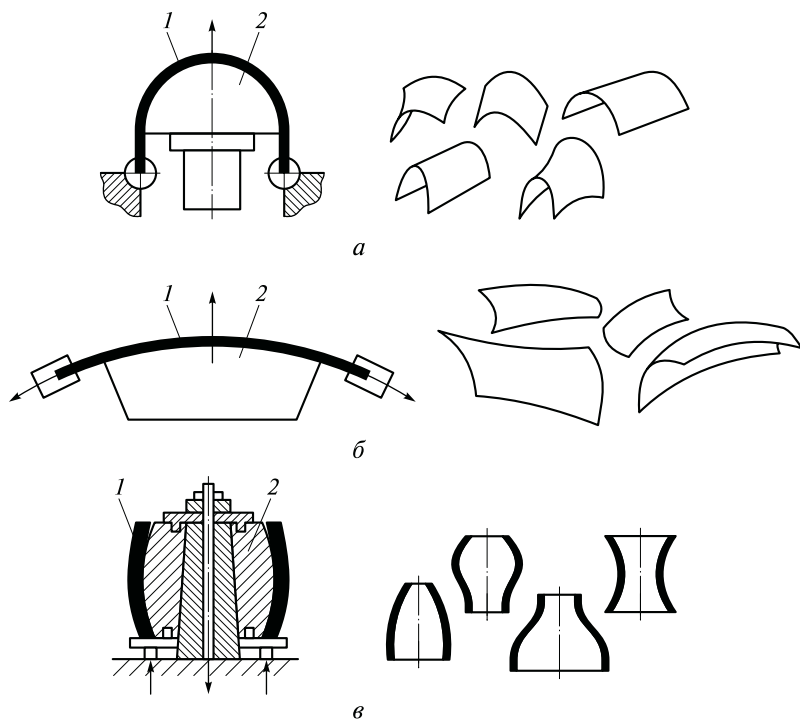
Схема формообразования деталей из листа обтяжкой:
